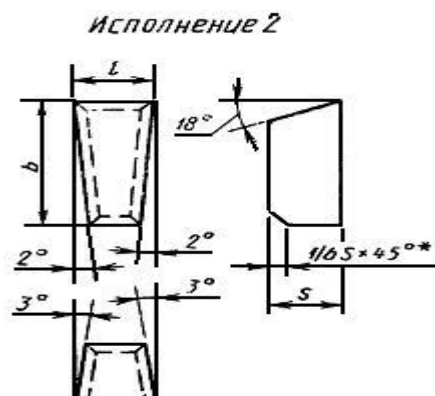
Эскиз пластины прорезного, (канавочного) резца
